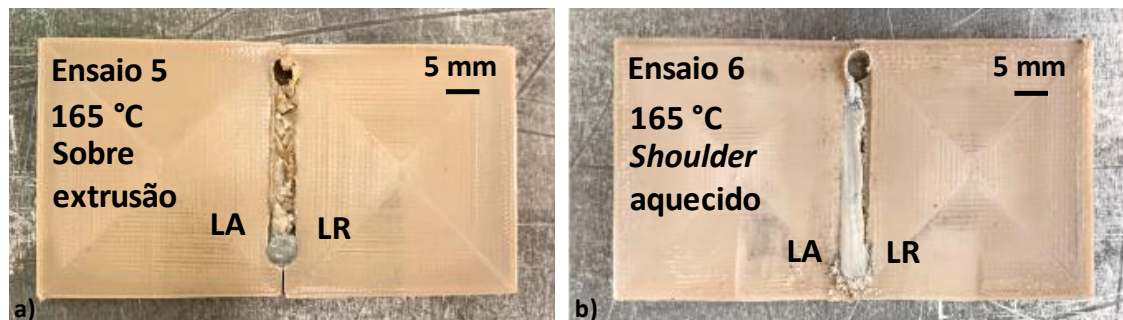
Aspeto visual da superfície das placas soldadas de PEEK: a) Ensaio 5, b) Ensaio 6.
